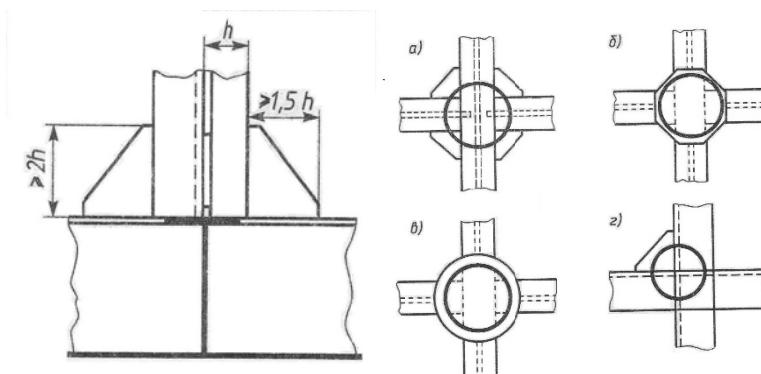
Вузол кріплення стопи пілерса на перетині рамного набору
